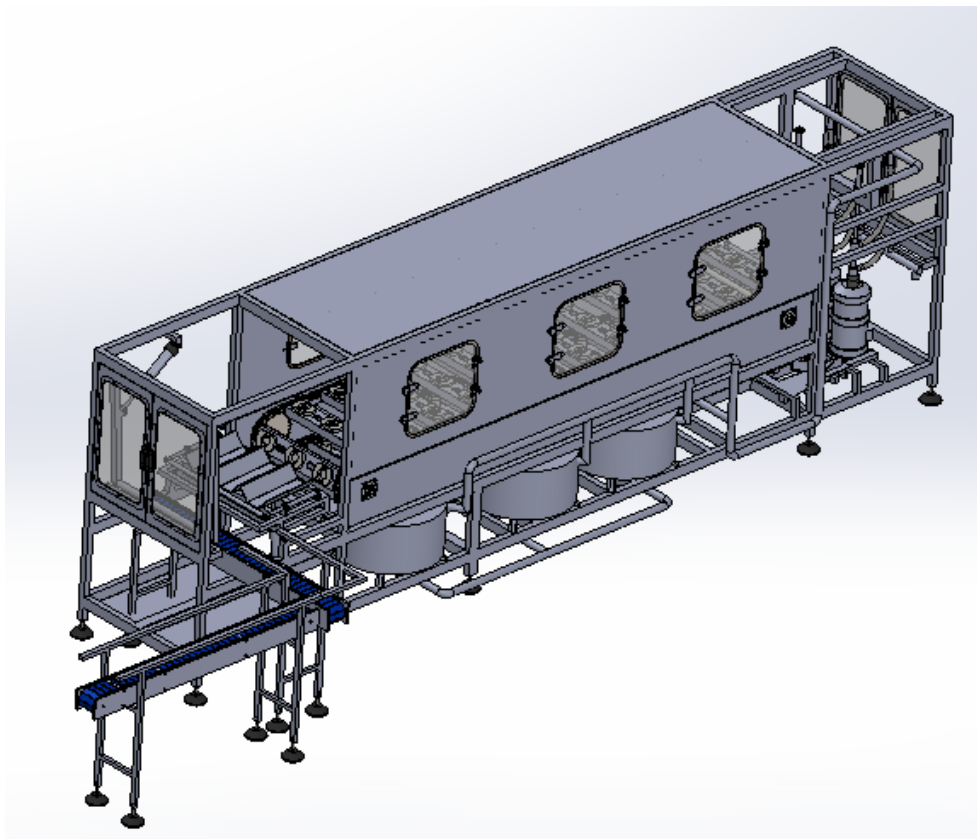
Diseño CAD de la máquina de lavado y llenado
